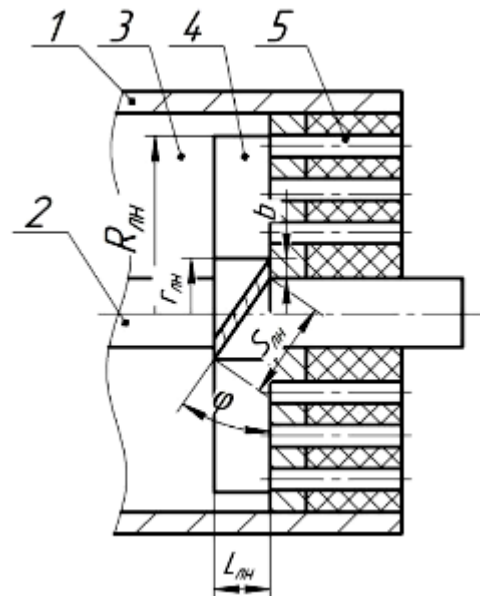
До визначення потужності, що витрачається на опір лопатевого ножа: 1 корпус; 2 - вал шнека; 3 - зона пластикації; 4 - лопатевий ніж; 5 - матриця
